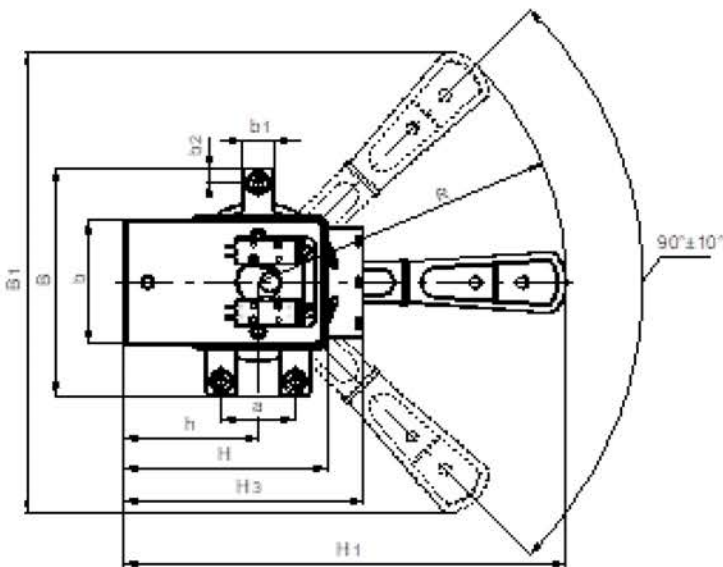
Выключатель-разъединитель трехполюсный на одно направление с боковой смещенной рукояткой.
